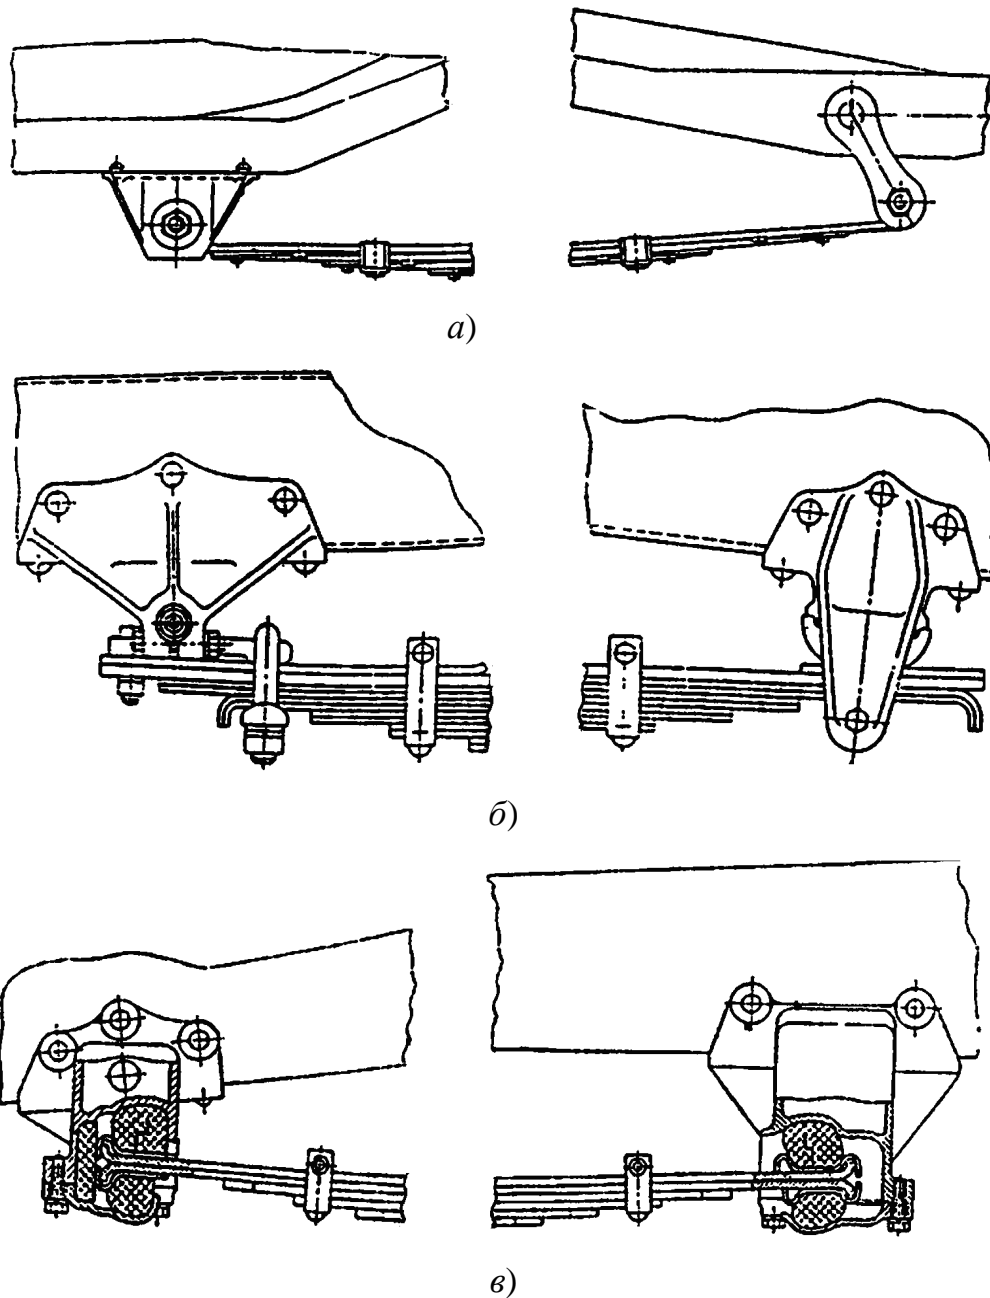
Основные способы крепления концов рессоры [128, 162, 304]:
